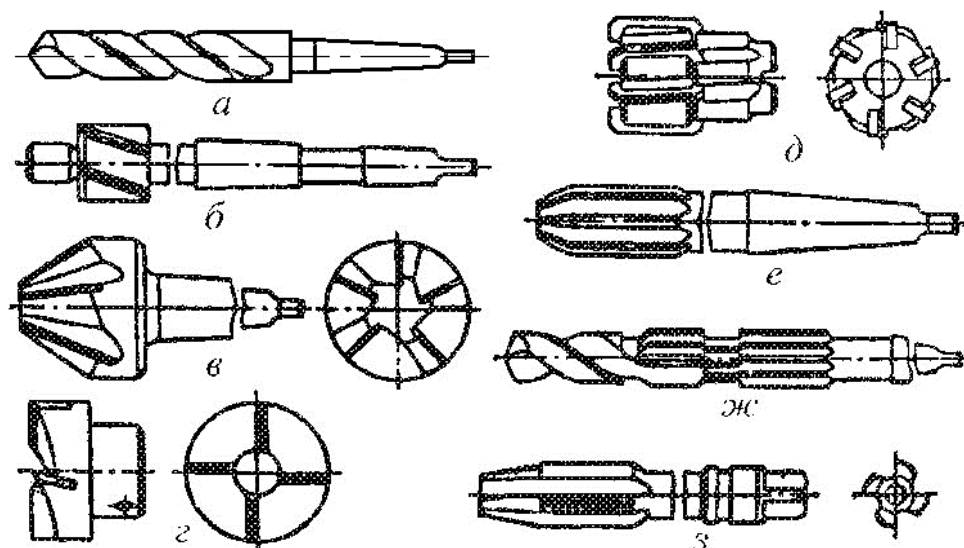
Інструменти для обробки отворів на свердлильних верстатах
